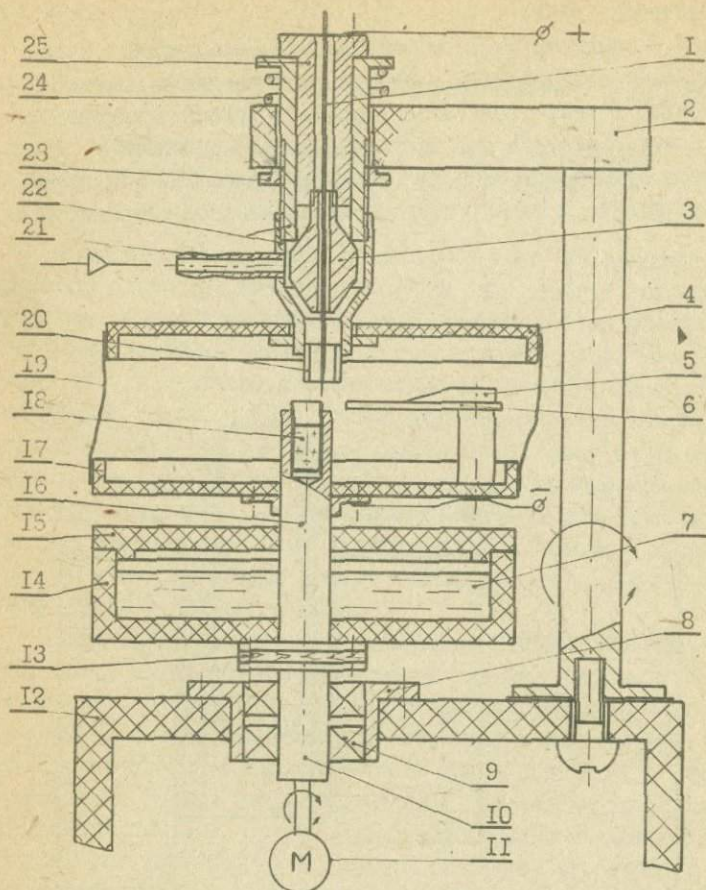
Устройство для охлаждения и полуавтоматической сварки ампул.
